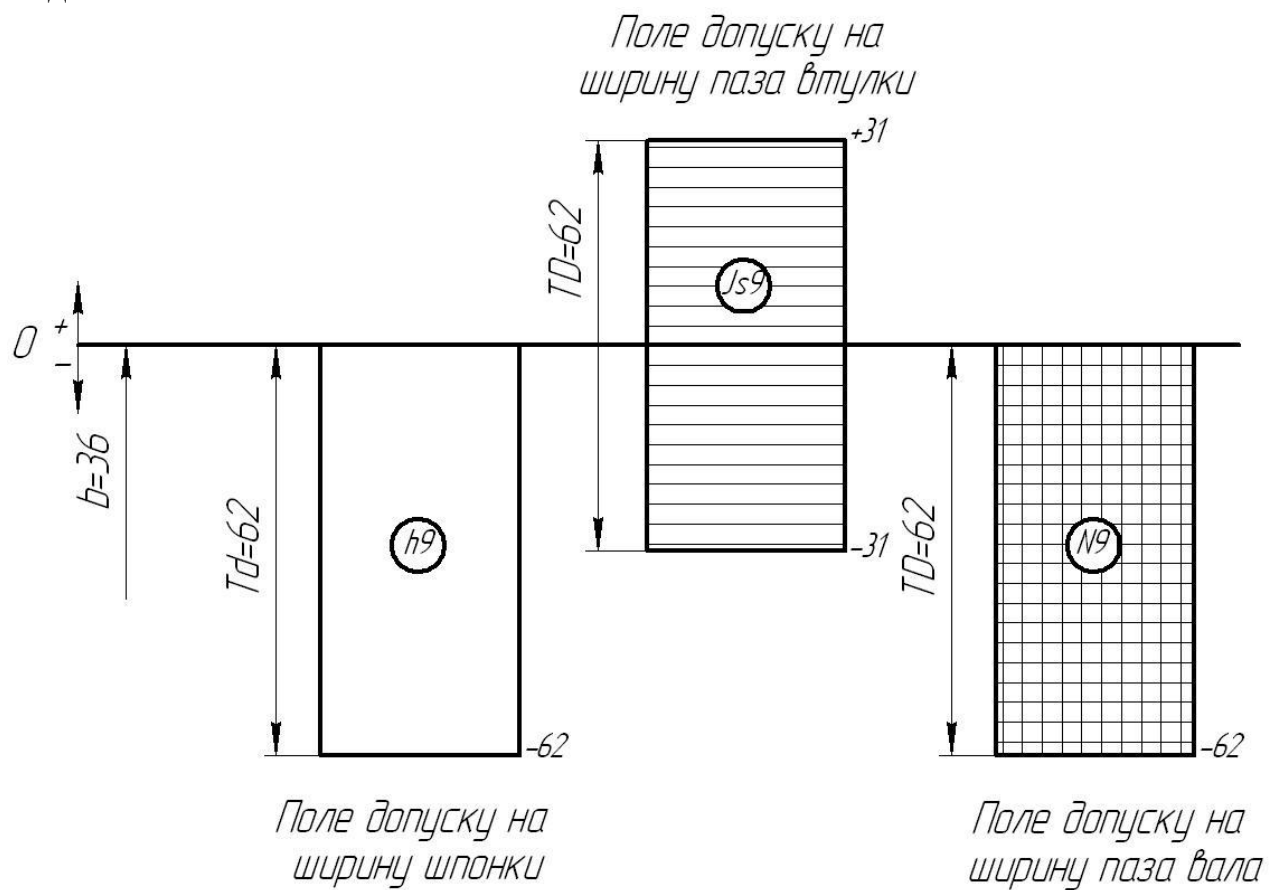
Схема розташування полів допусків шпонкового з'єднання
